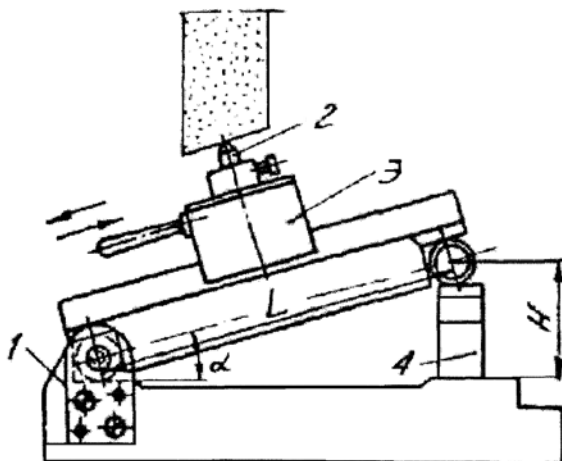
Синусное приспособление для правки шлифовальных кругов:
